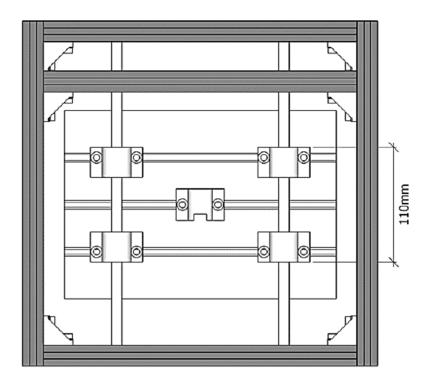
Vista inferior de mesa de trabajo con soportes y guías instalados.
